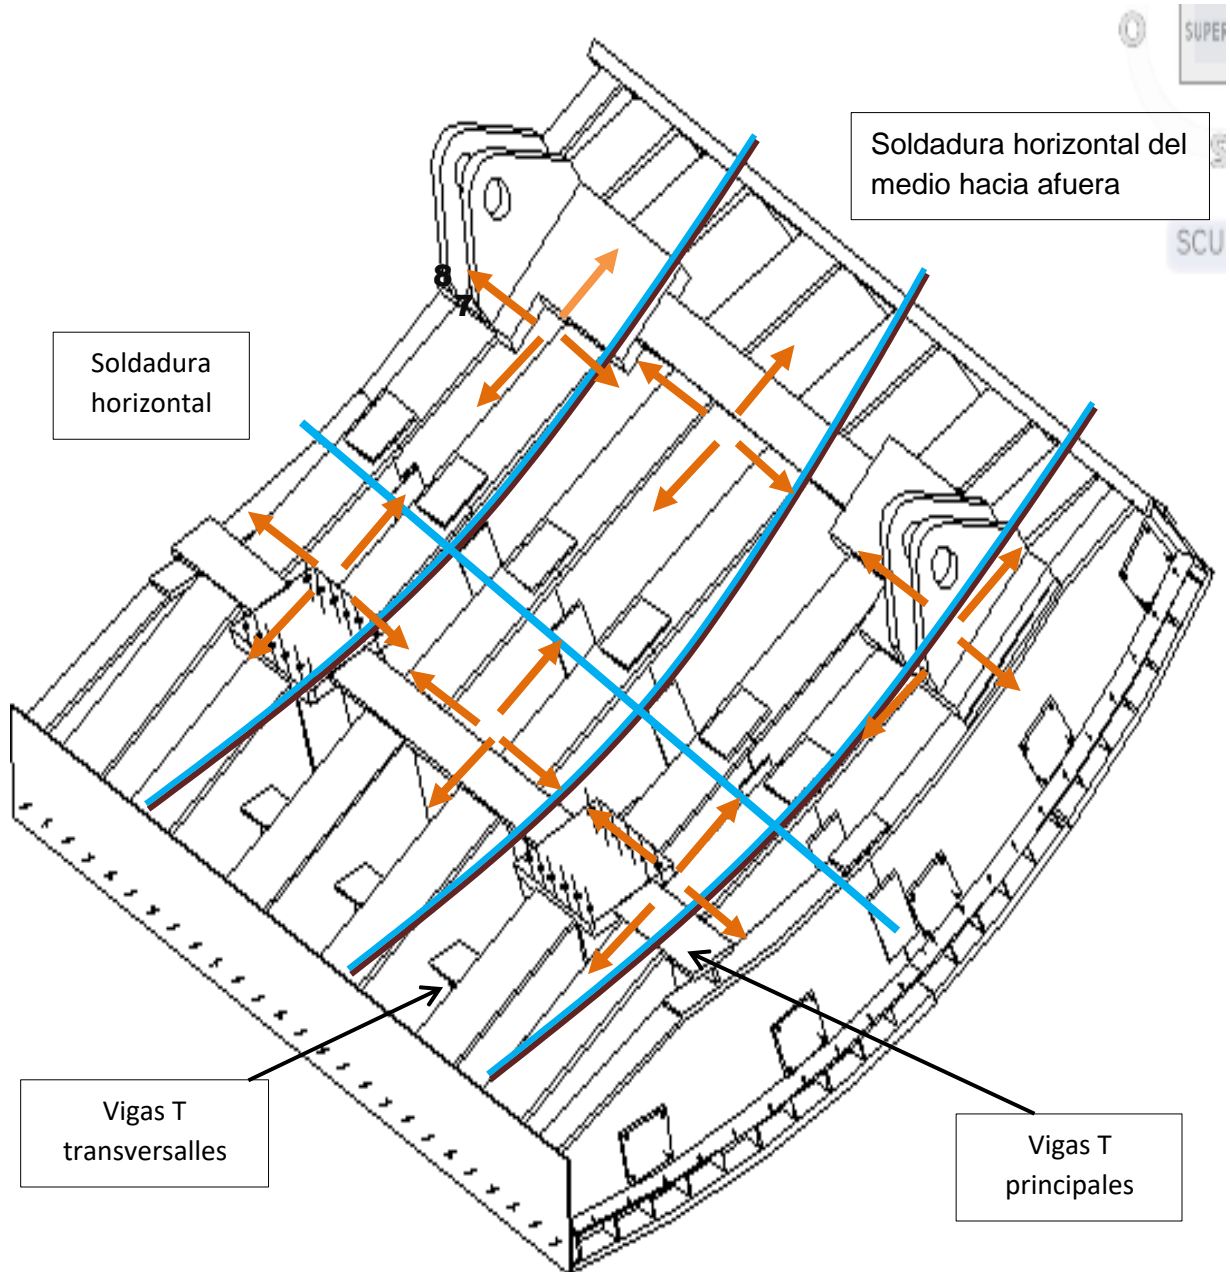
Primer Soldeo Horizontal, desde las vigas "T" principales hasta las vigas "T" transversales intercalados. Fuente: Propia.
